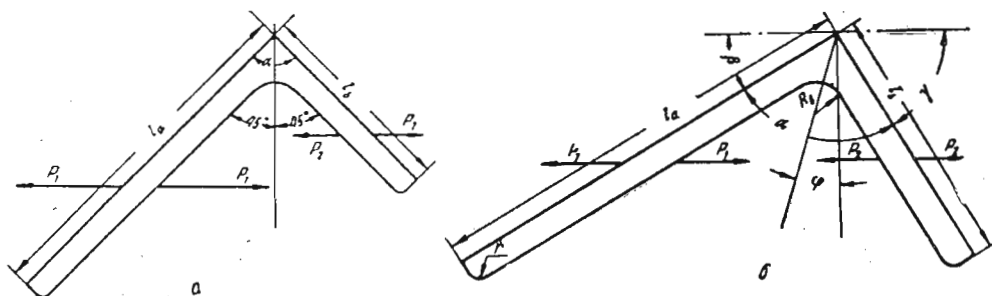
Профиль неравнобокой угловой стали и расположение его в чистовом калибре:
